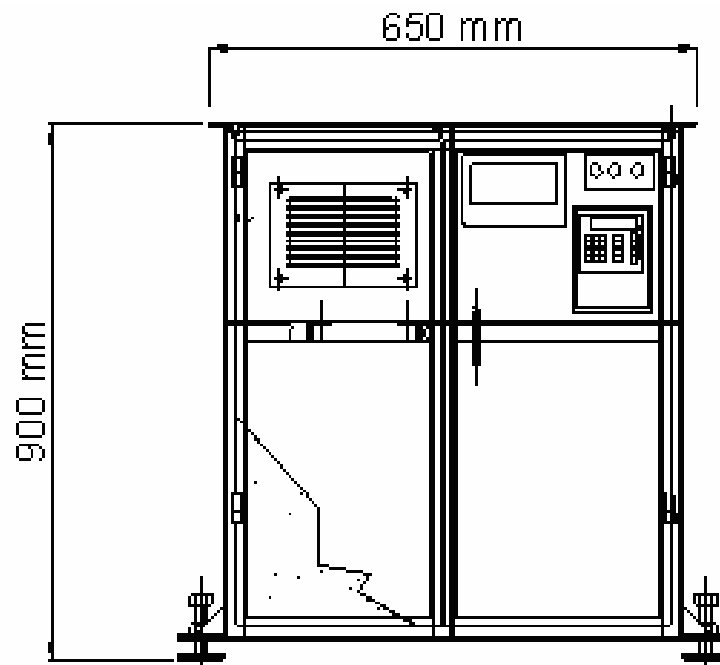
Mesa que será la base de la “Maquina tribológica de configuración geométrica de cilindros cruzados para análisis de desgaste adhesivo”.
